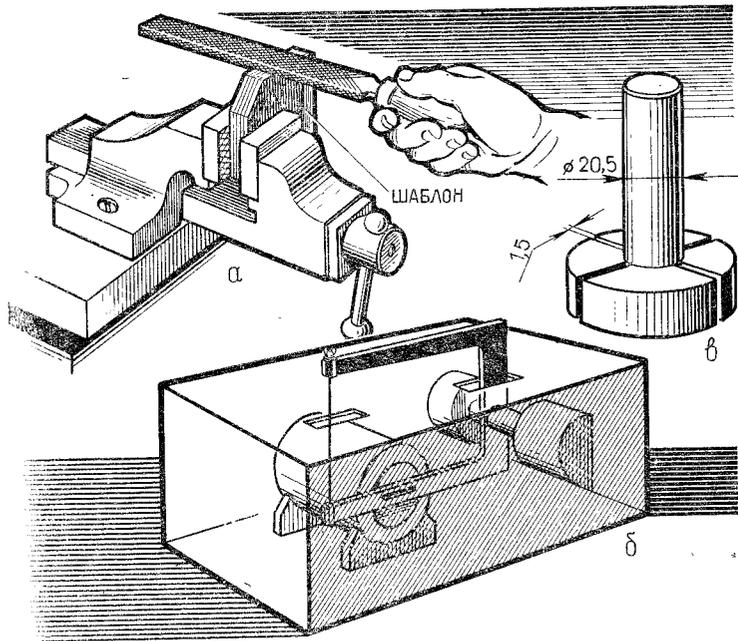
Изготовление пластинчатых стабилизаторов: а — пакетом по шаблону; б — на механическом лобзике; в — стапель для установки пластинчатых стабилизаторов
